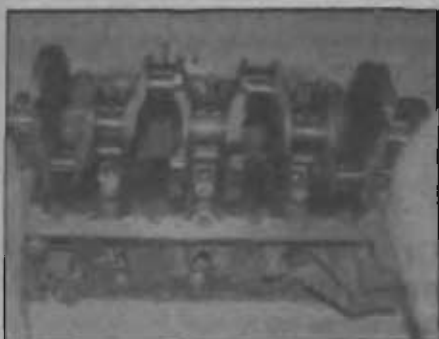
Установка коленчатого вала в блок цилиндров двигателя 1,8 л
